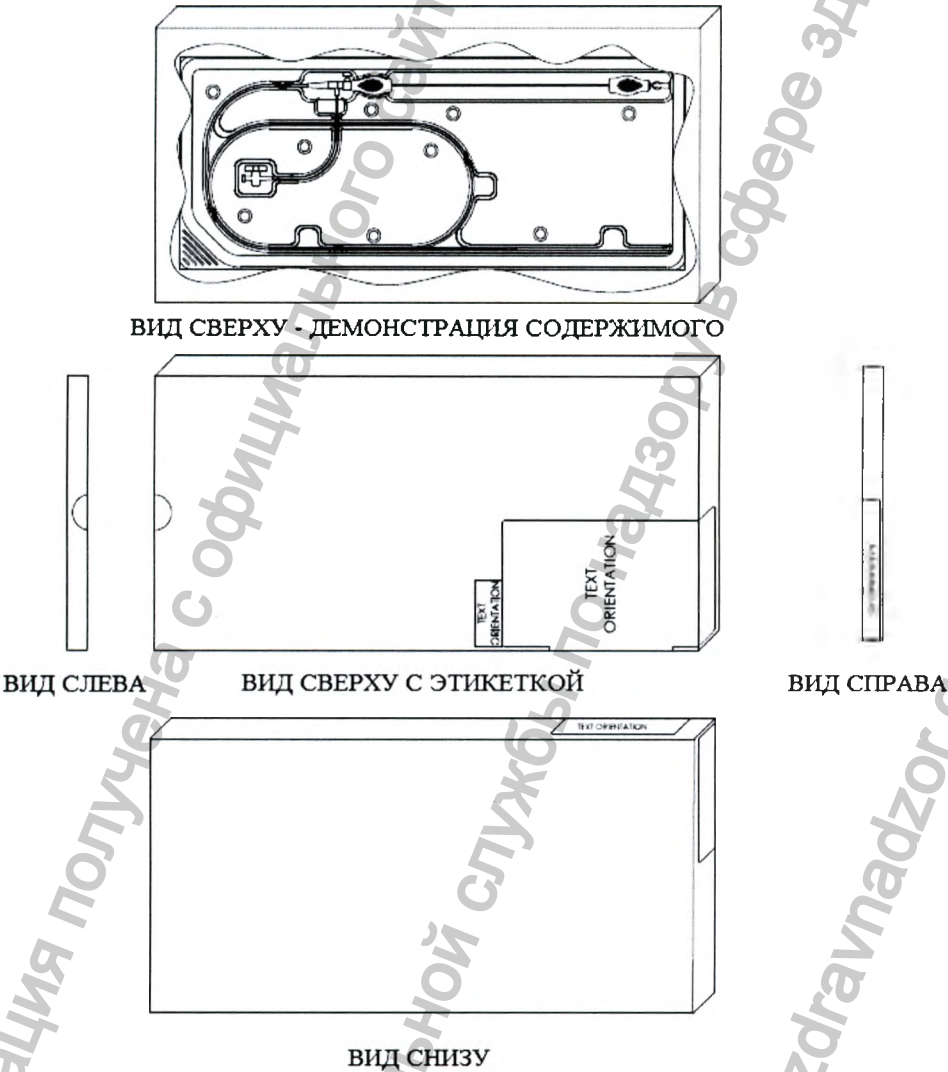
Чертеж вторичной упаковки (общий вид)
